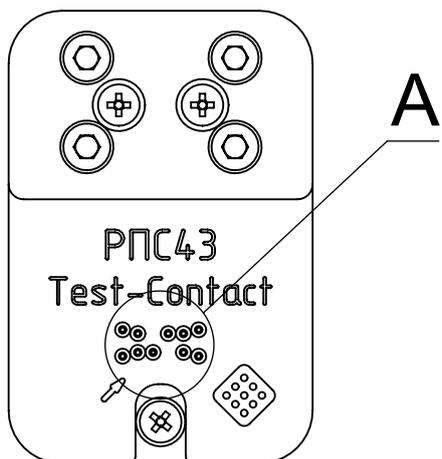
Габаритные размеры КУ (вид сверху без трубины)
